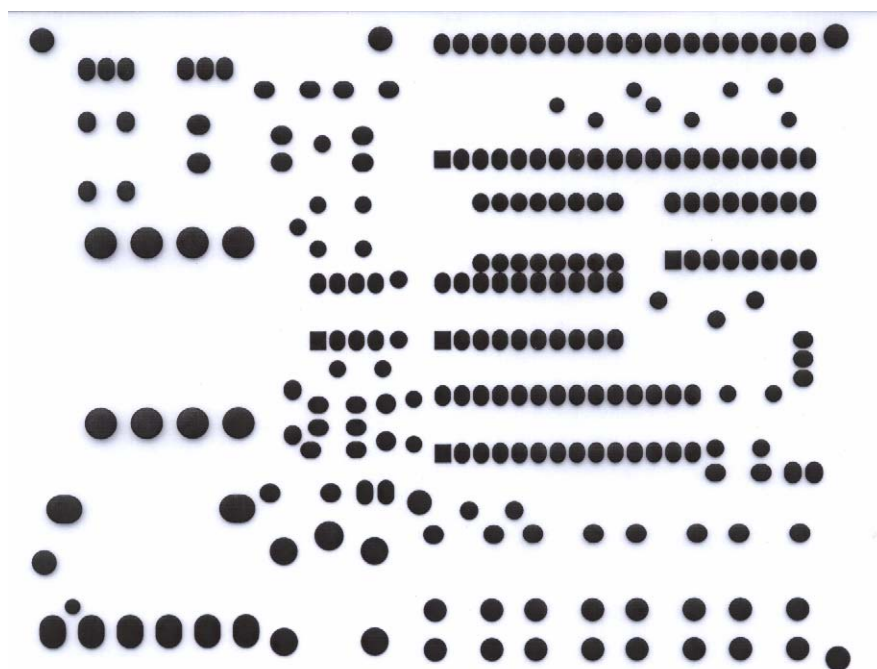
Mascara de solda da placa de circuito impresso.
